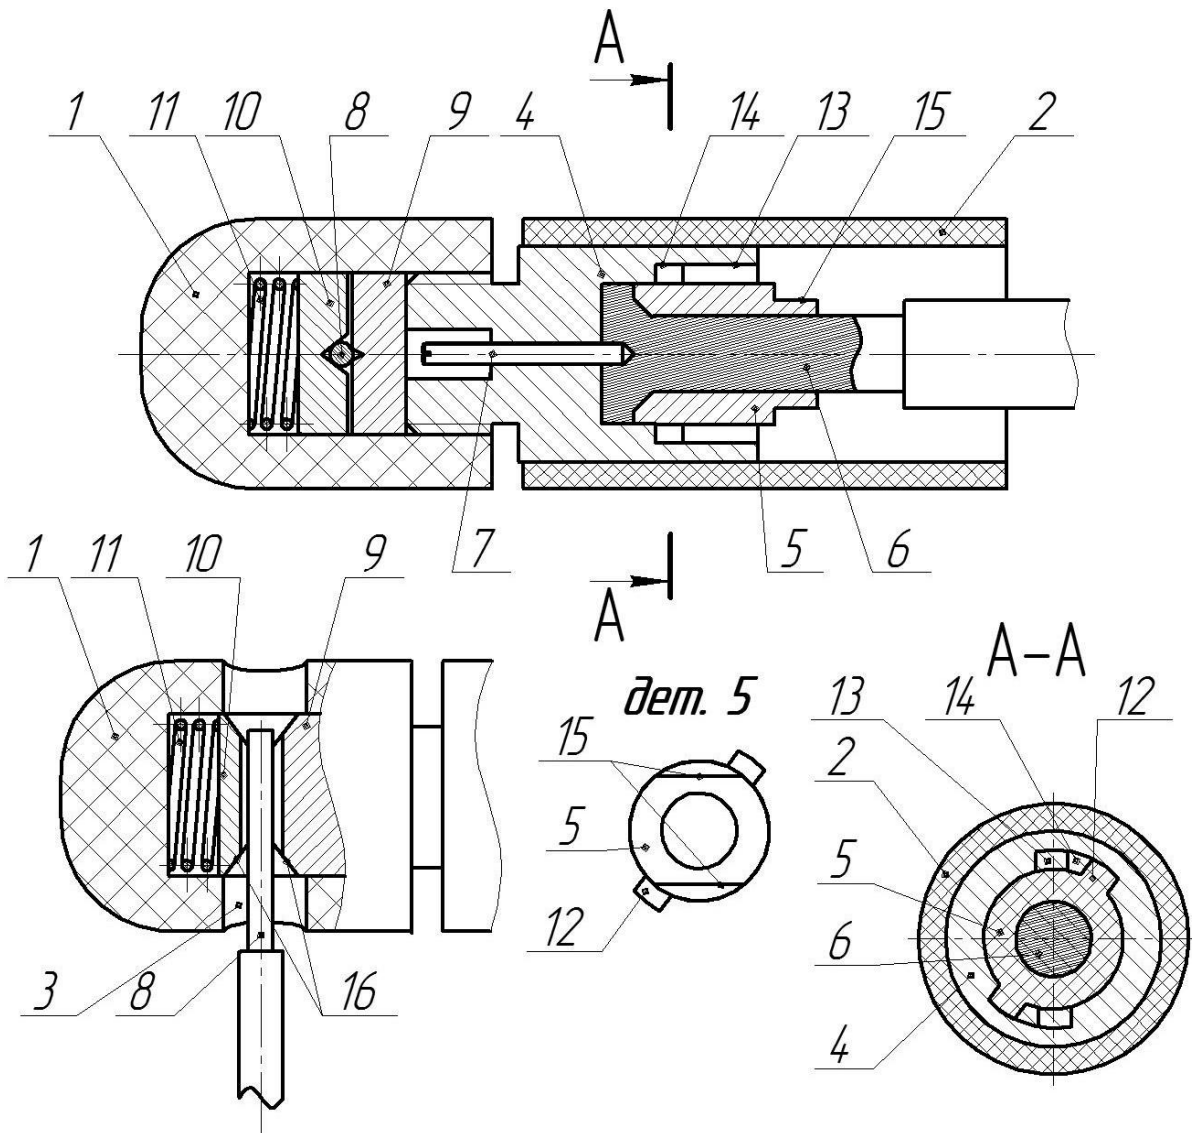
Конструктивна схема електродотримача для ручного дугового зварювання
